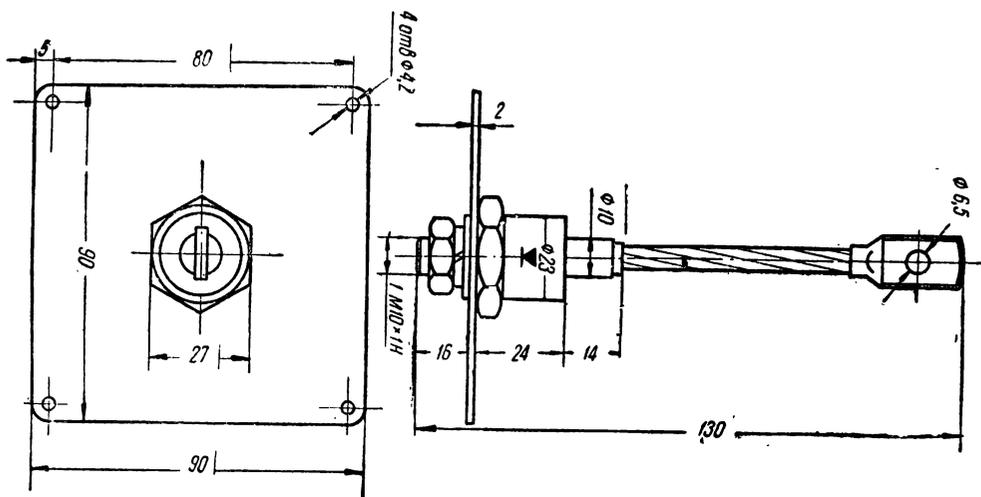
Габаритные размеры кремниевого вентиля ВК-25
